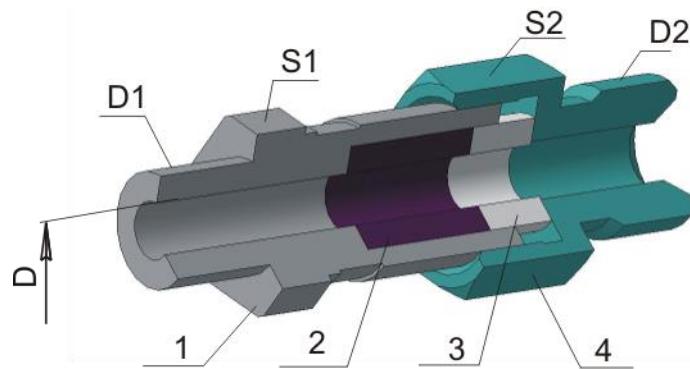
Конструкция кабельного ввода для монтажа кабеля в трубе
